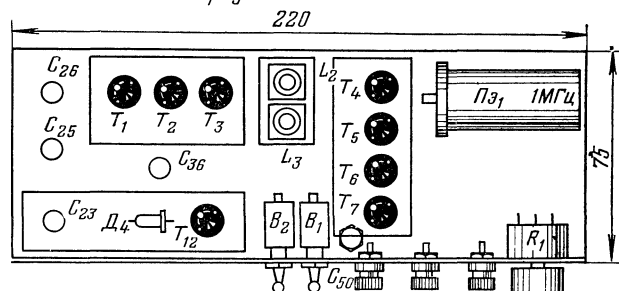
Расположение деталей на шасси генератора (вид сверху).
